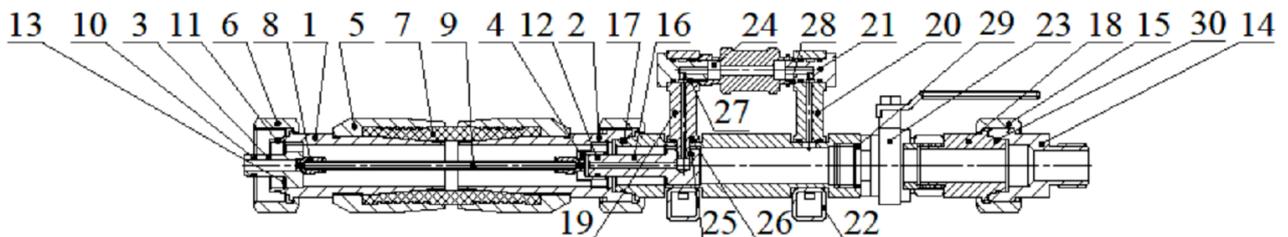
а. Рукав присоединительный с узлом управления - ИП 4605АР
